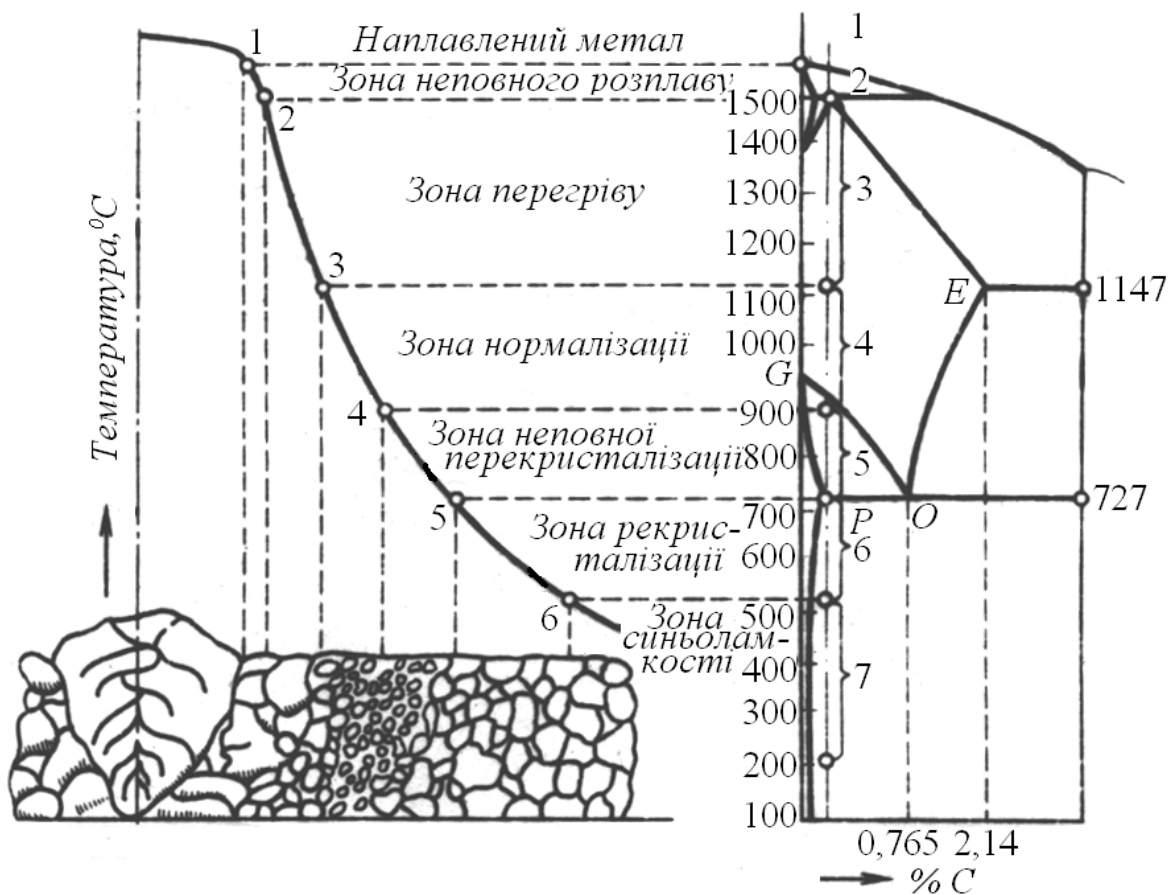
Схема утворення структури зварного шва для низьковуглецевої сталі
